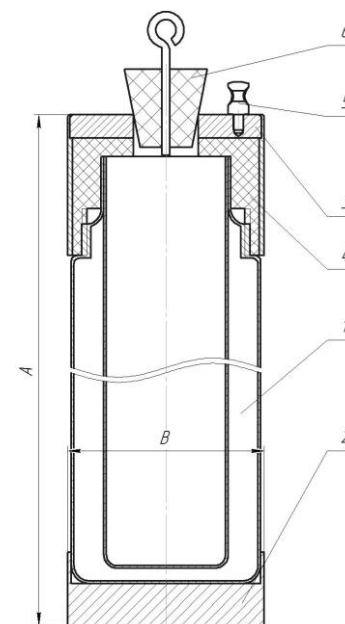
Пробоотборник термостатированный типа ИЗОТЕРМ: 1 – корпус, 2 – донце, 3 – крышка, 4 – вставка крышки, 5 – бобышка, 6 – пробка со штоком для крепления металлического троса.
